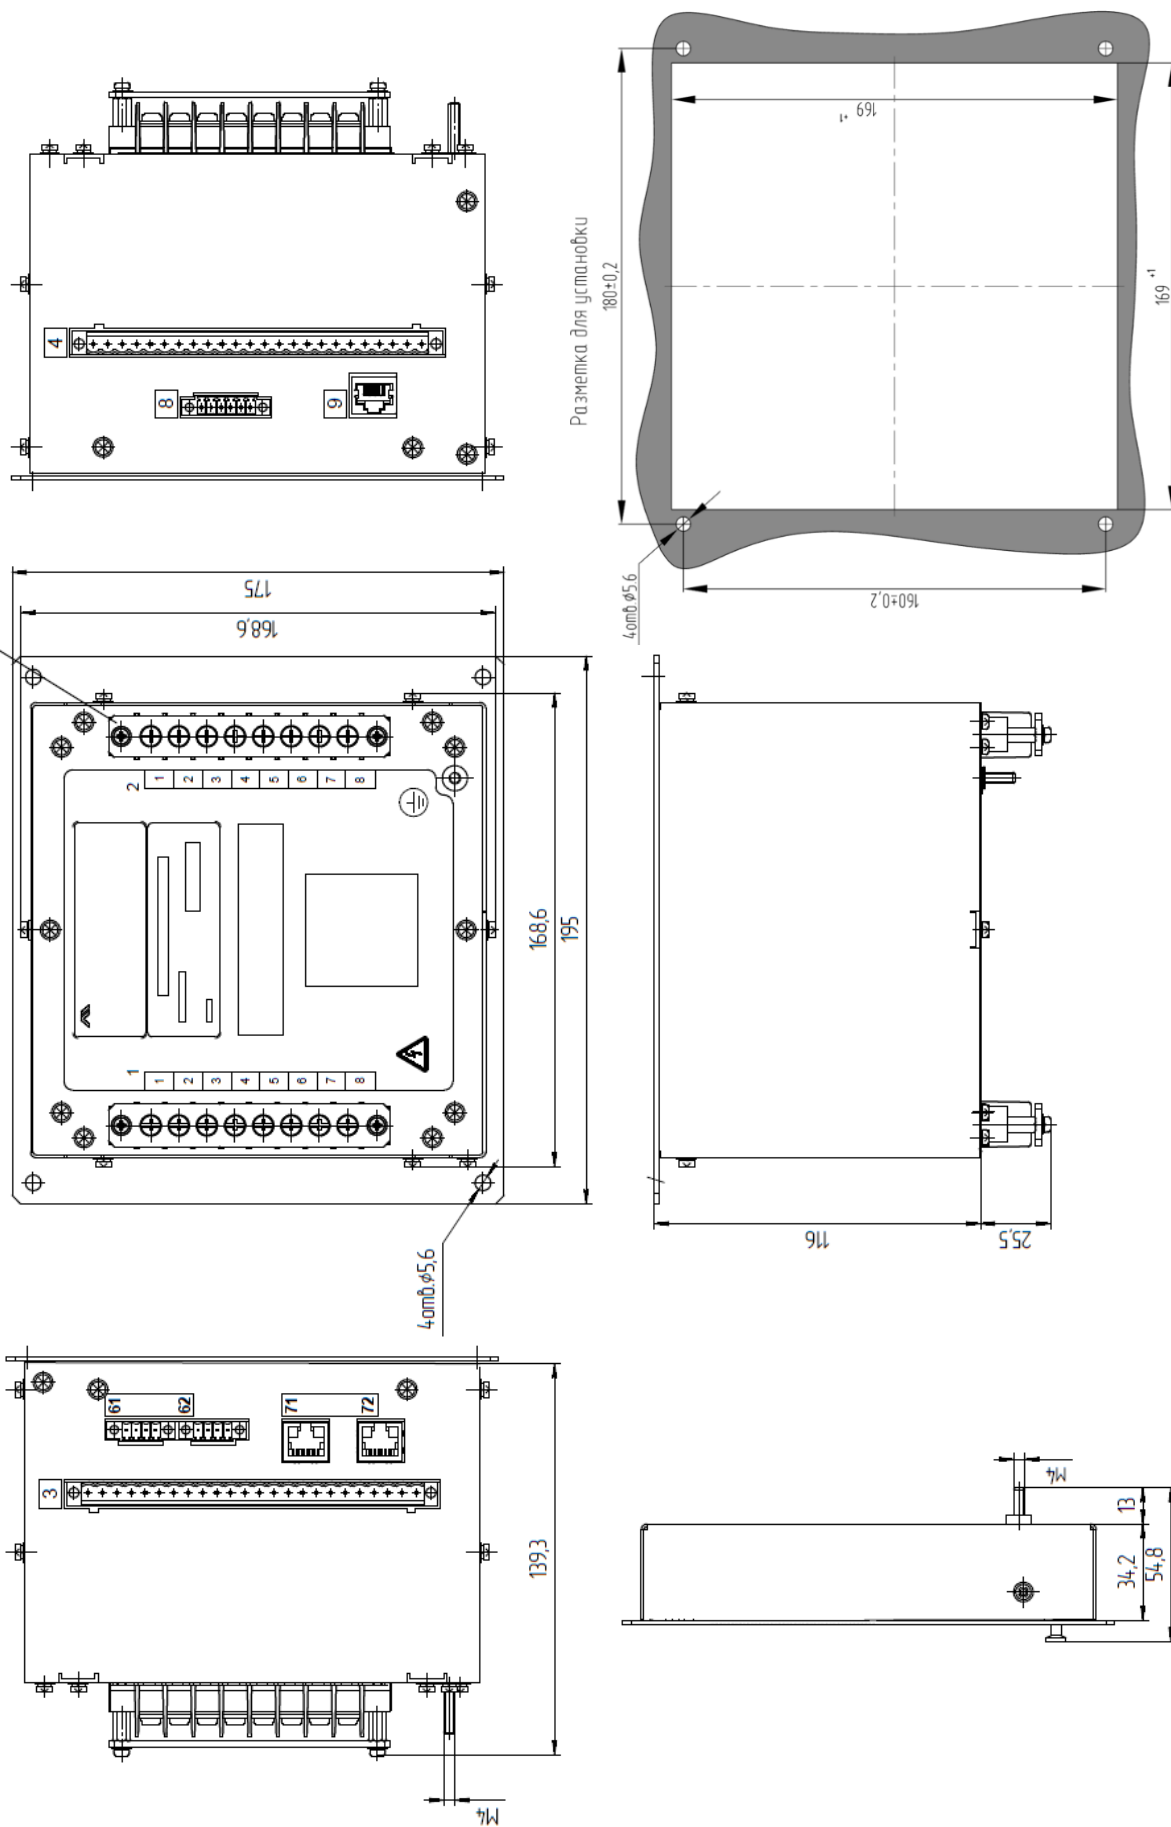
(лист 1 из 5 а) - Габаритные и установочные размеры блока ДИВГ.648228.123
